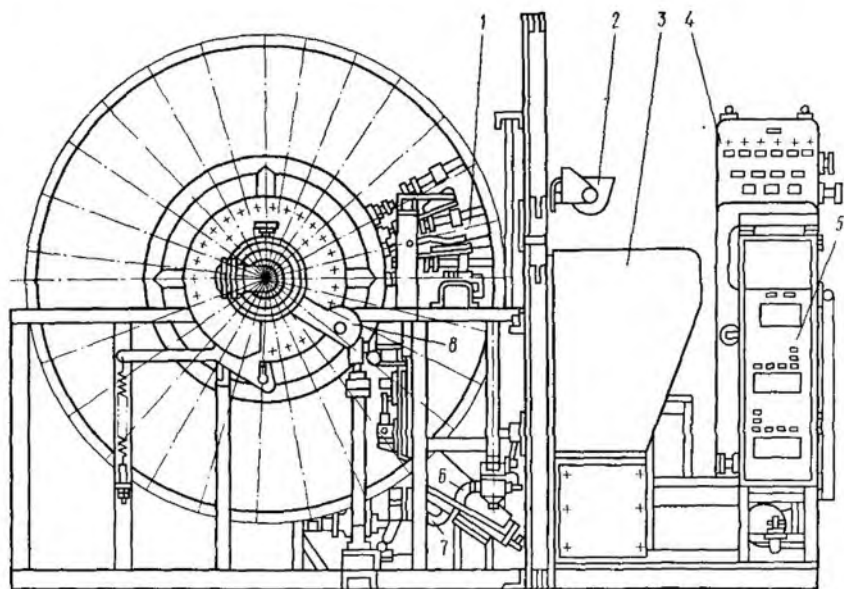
Автоматизированный роторный морозильный аппарат типа АРСА-3-15Р:
